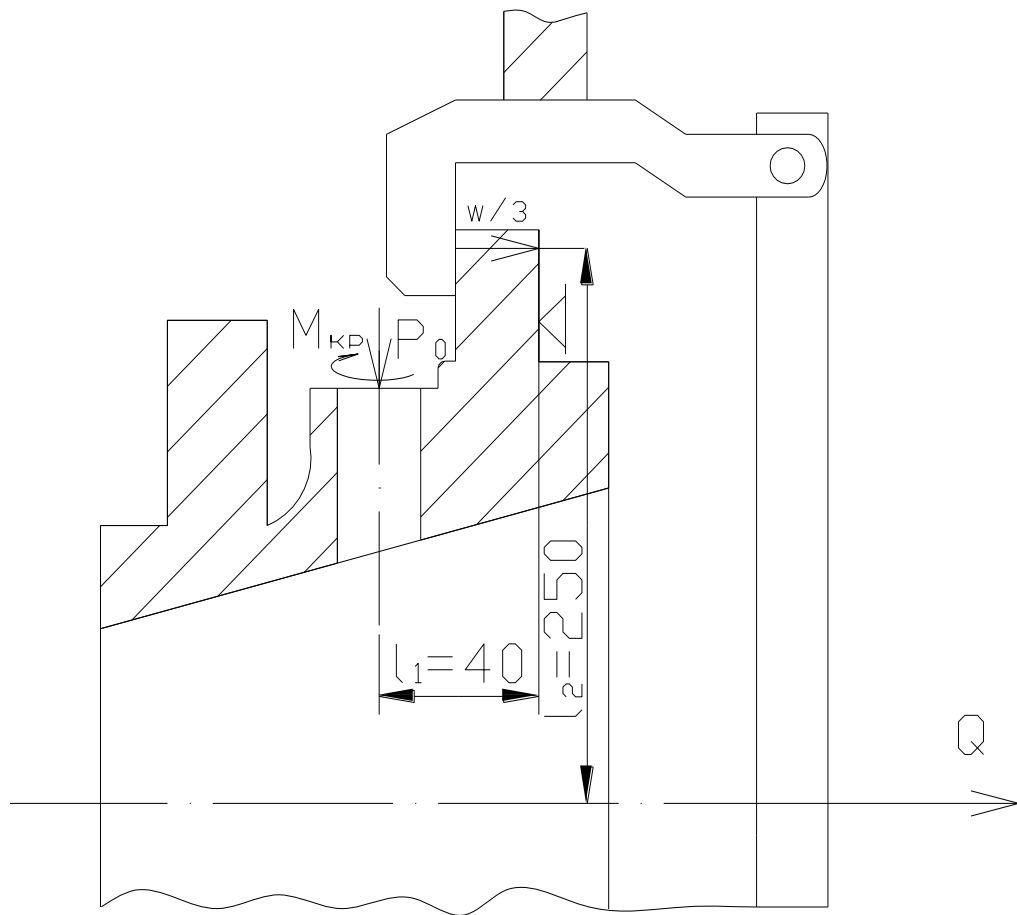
Схеми дії сил на заготовку під час обробки
